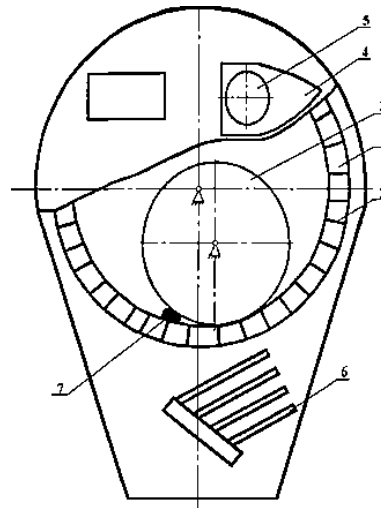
Схема барабанно-ножового подрібнювача
